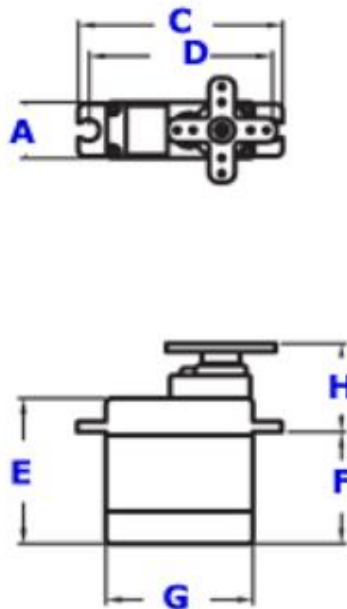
Основні конструктивні розміри сервомотора механізму тангажу платформи [56]
